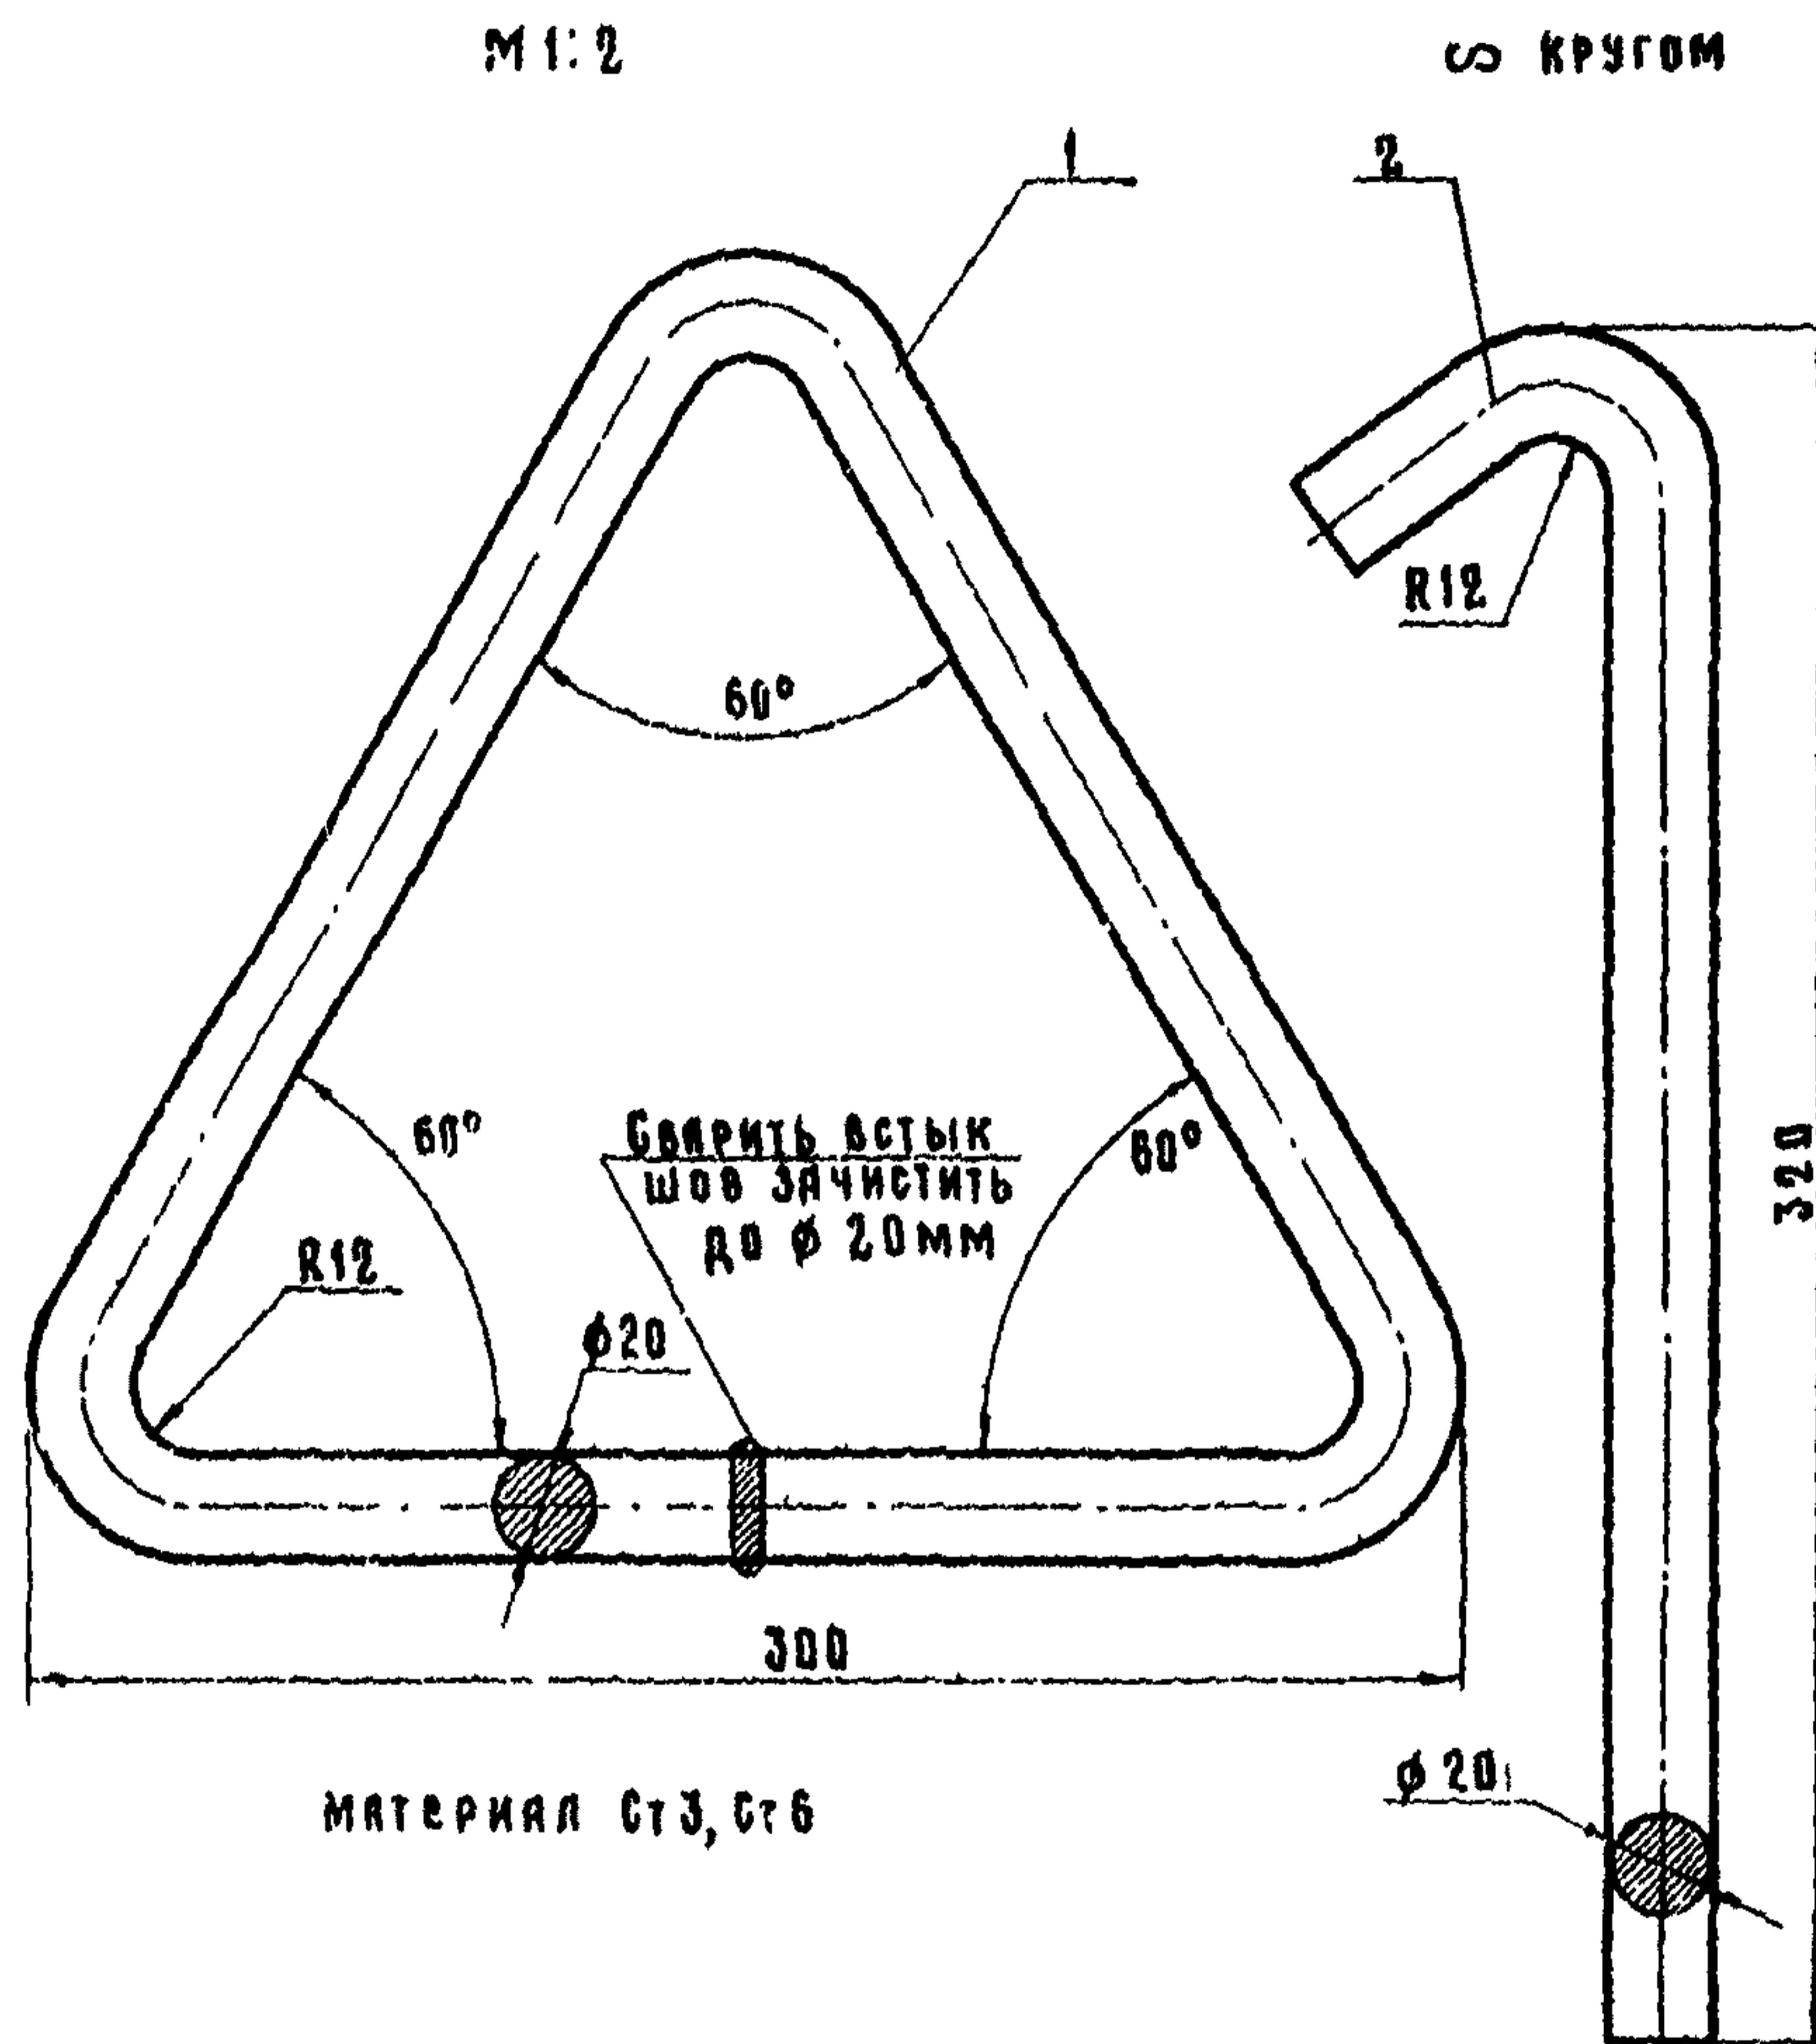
Грузозахватное приспособление для мягких контейнеров: 1 - треугольник-триверса; 2 - штырь
